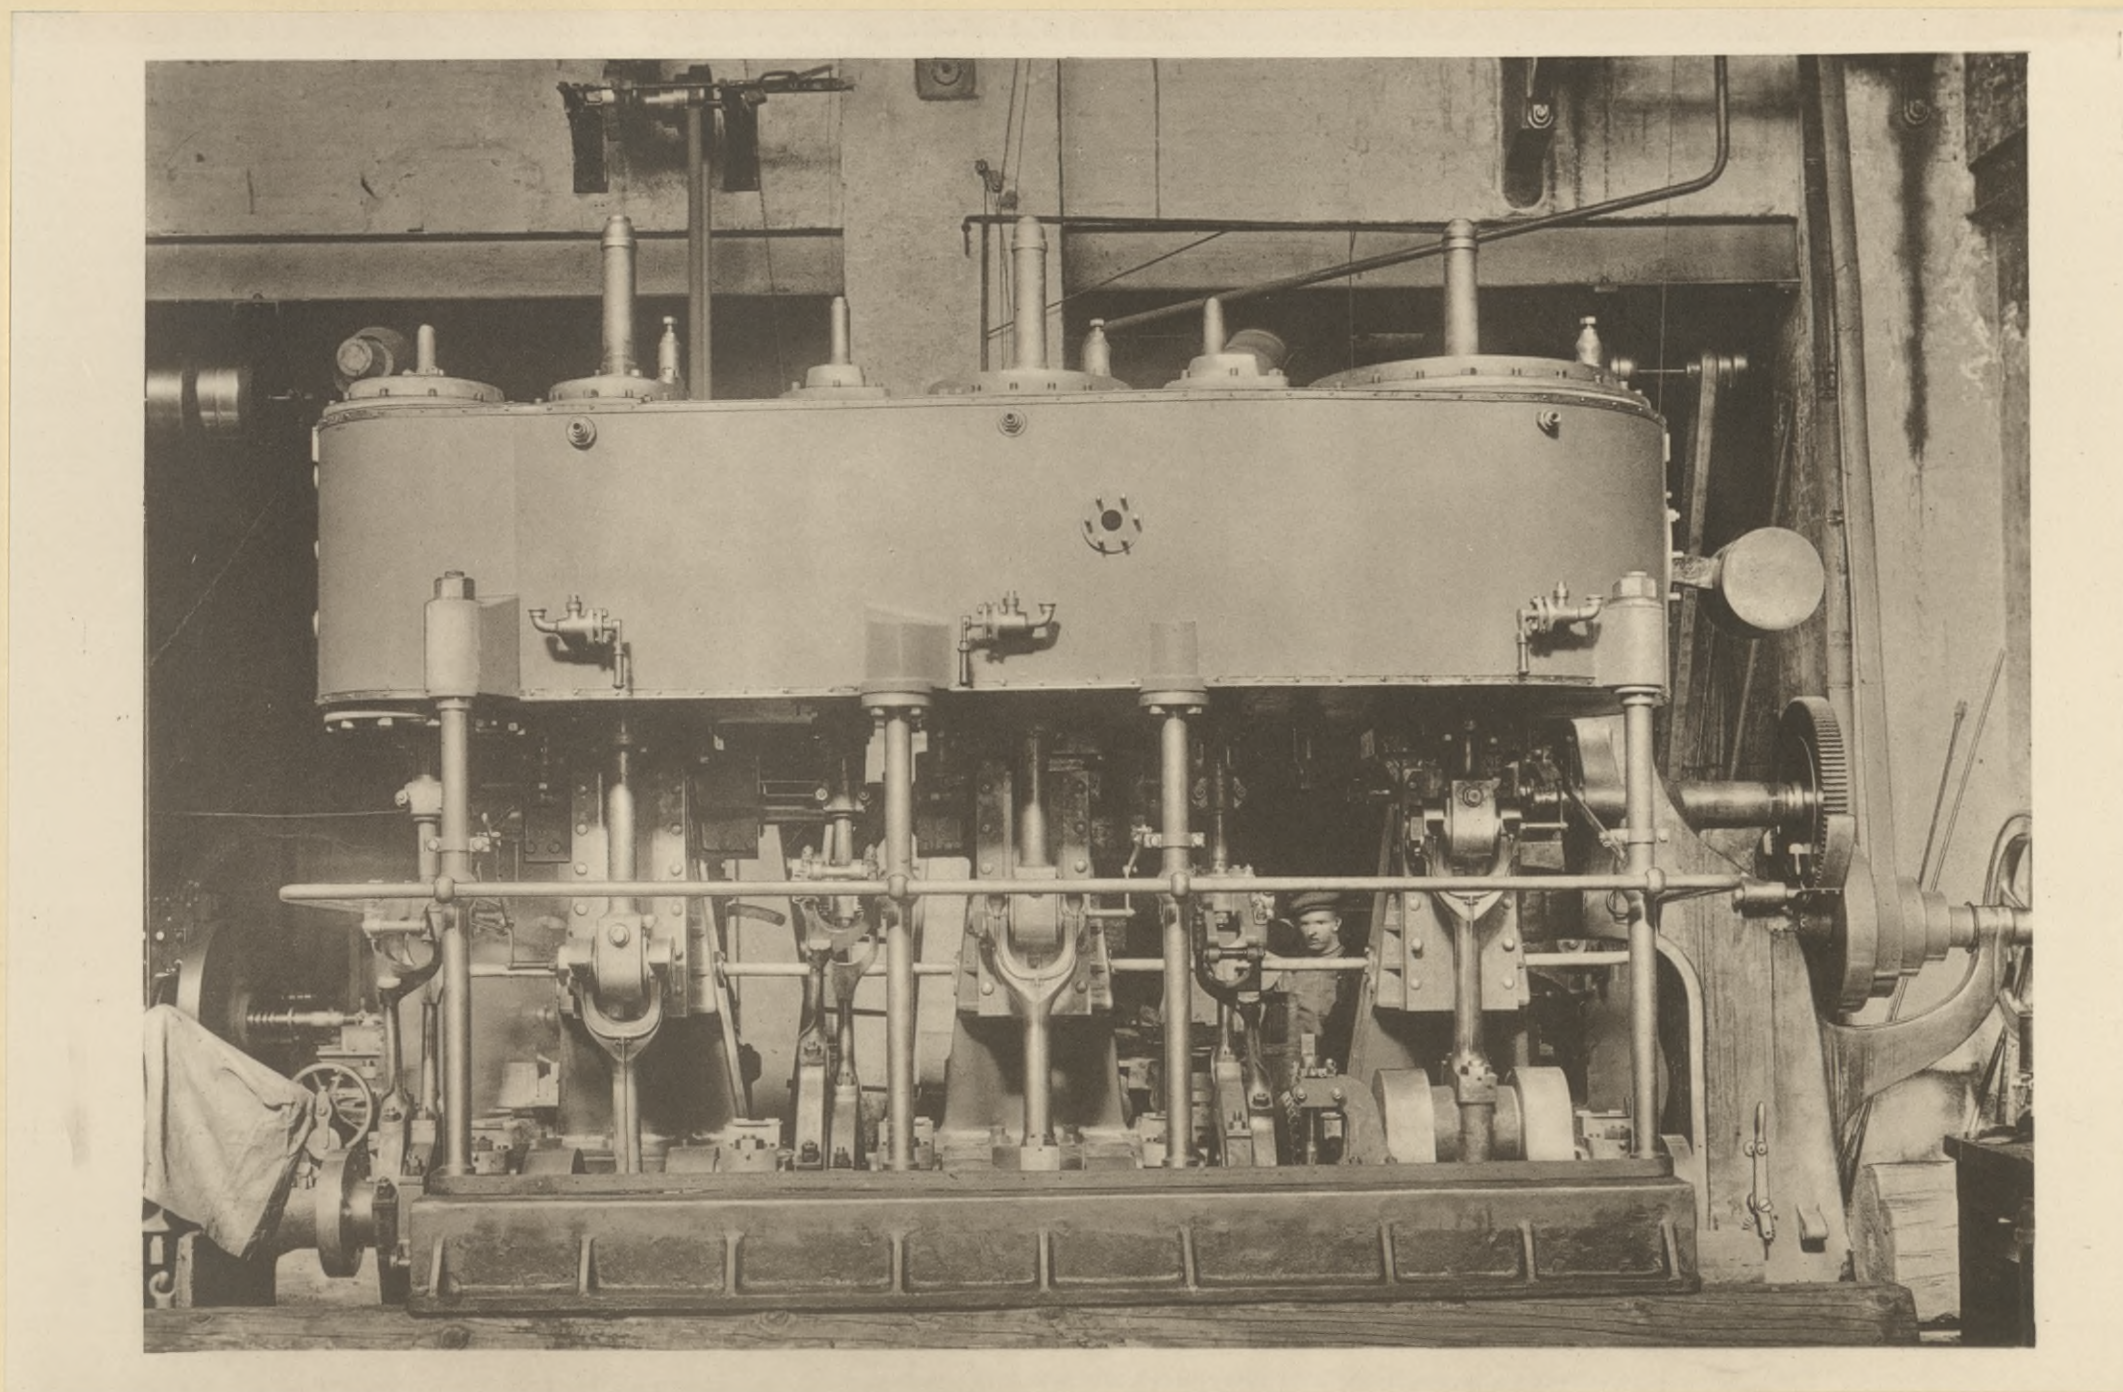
BACKBORDMASCHINE DES SAUGEBAGGERS „GALVESTON“, 600 indizierte HP.
